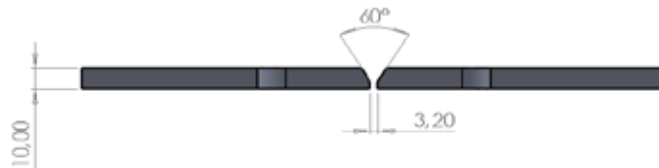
Bisel y espaciamento de probeta de tracción utilizado para la soldadura en V (Unidades en mm) utilizando SolidWorks.
